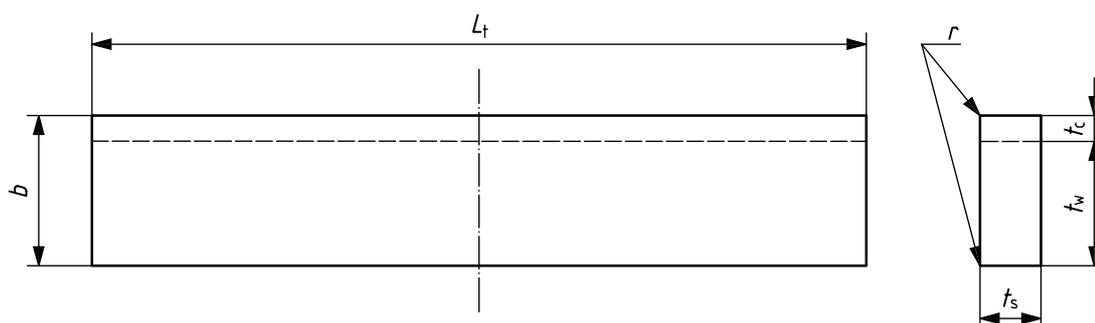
Éprouvette de pliage de côté sur revêtement sans soudure bout à bout (SBC)
